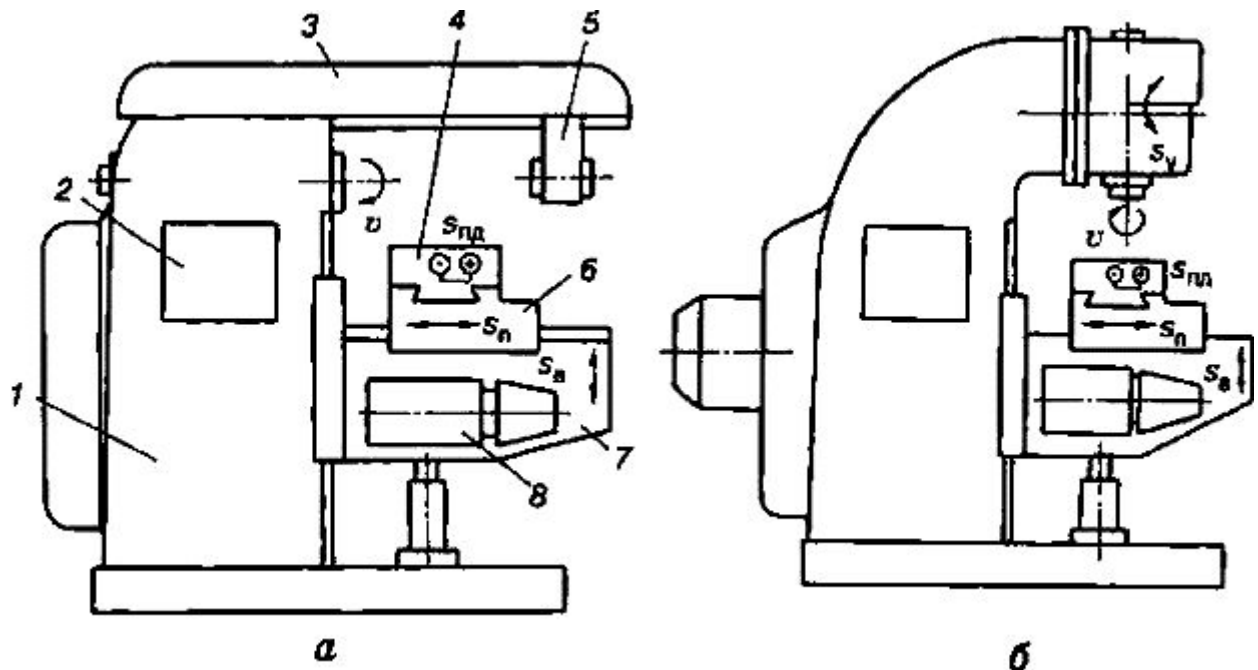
Консольні горизонтально-фрезерний і вертикально-фрезерний верстати
